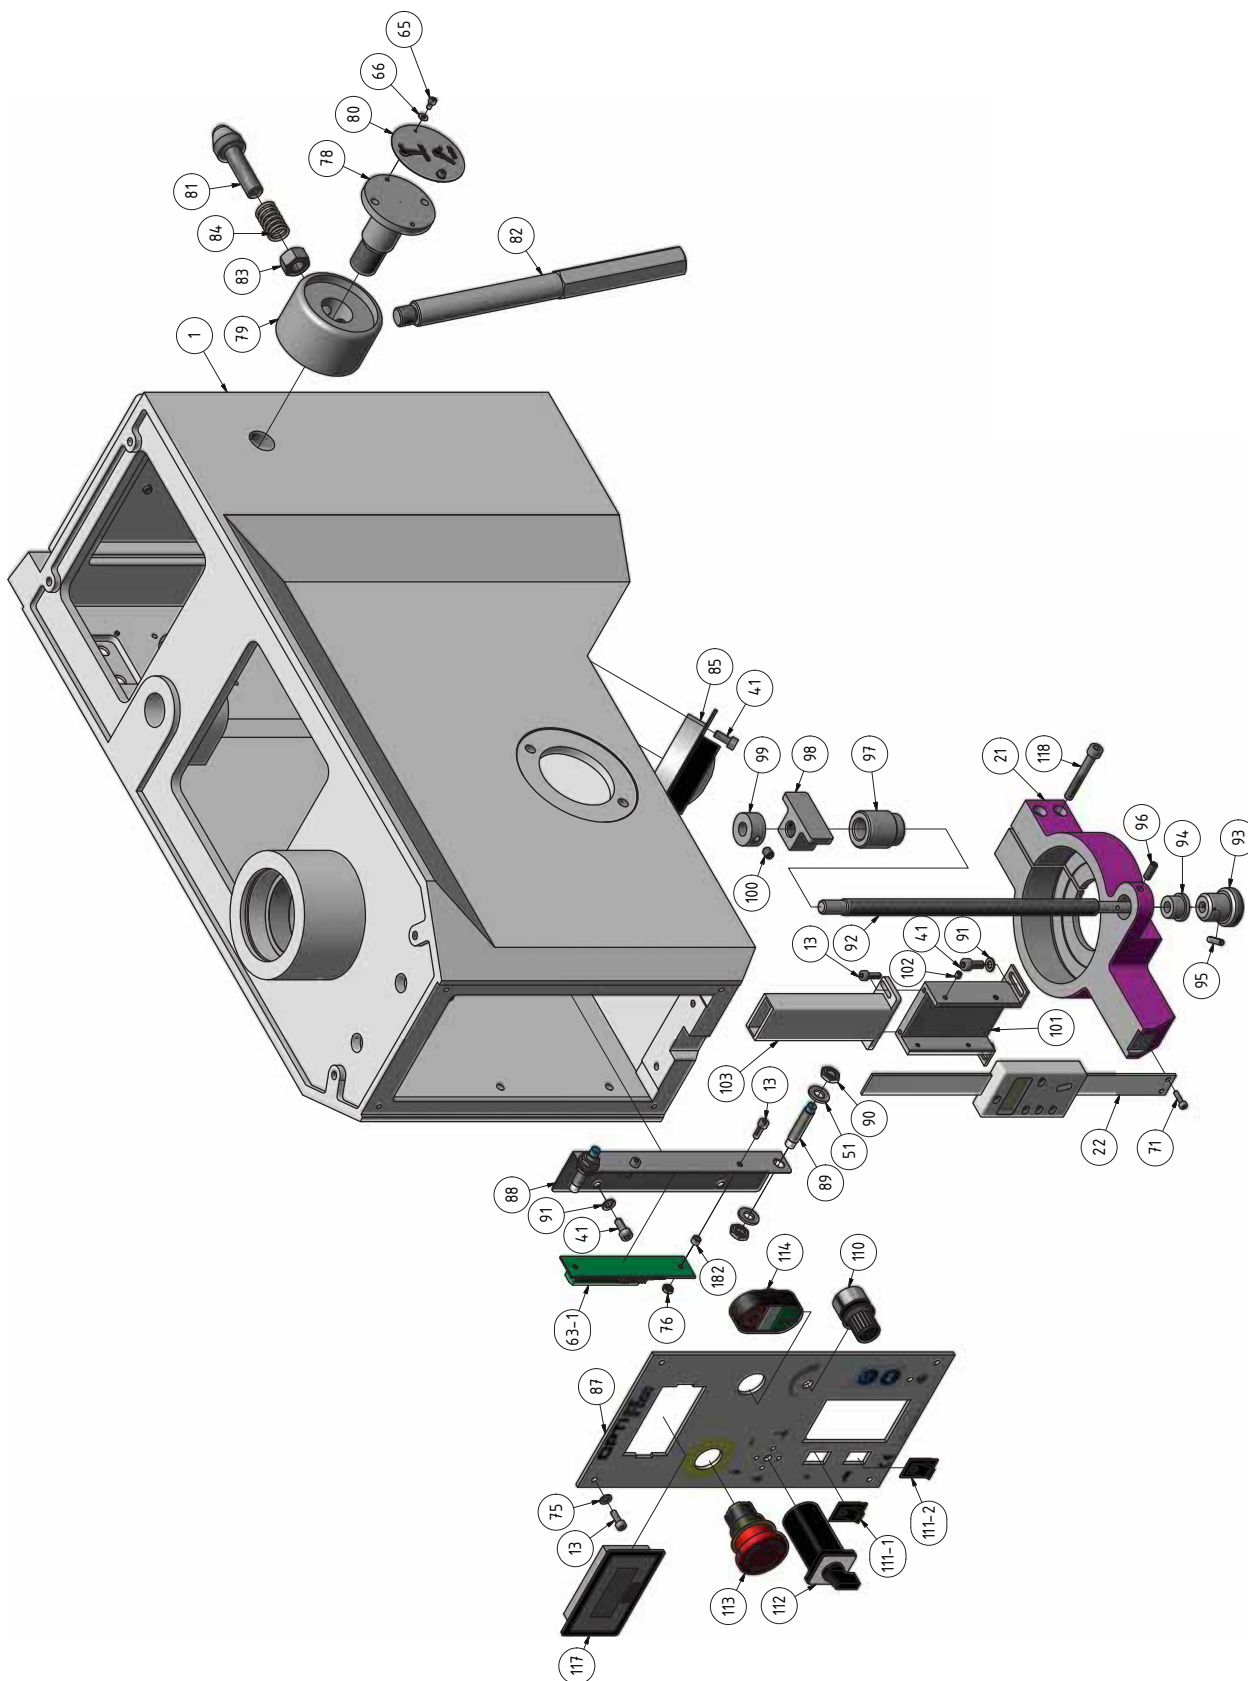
Bohrkopf 4 von 5 - Drilling head 4 of 5
